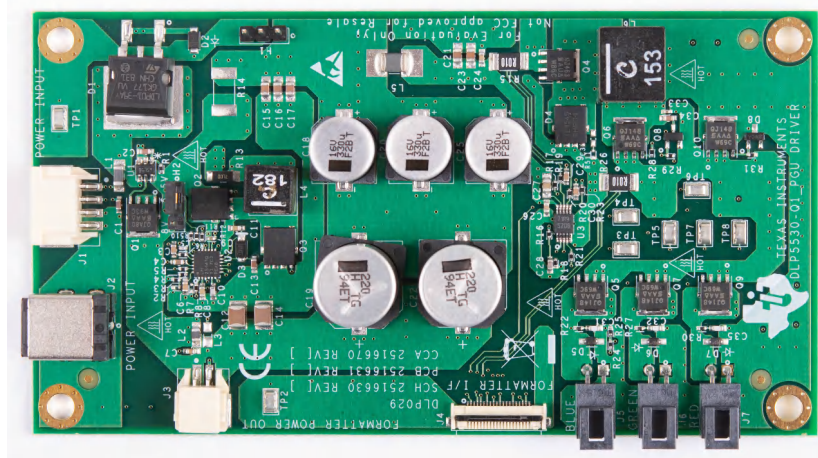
LED 驱动器 PCB - DLP4620SQ1EVM
